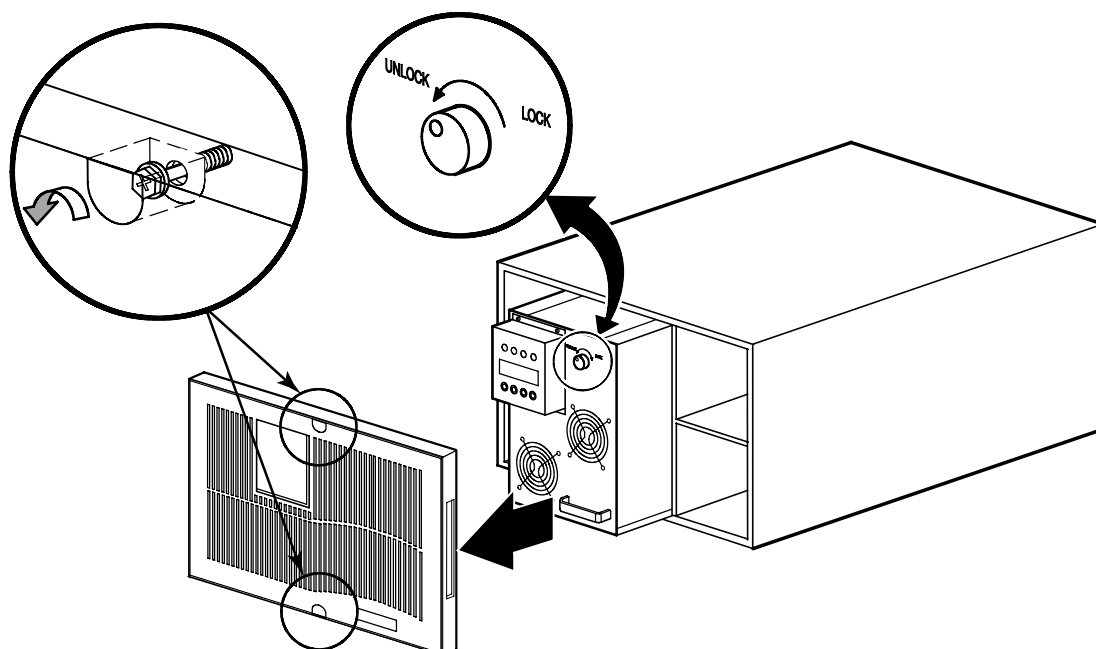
Rimozione del pannello frontale UPS e del modulo dei componenti elettronici
